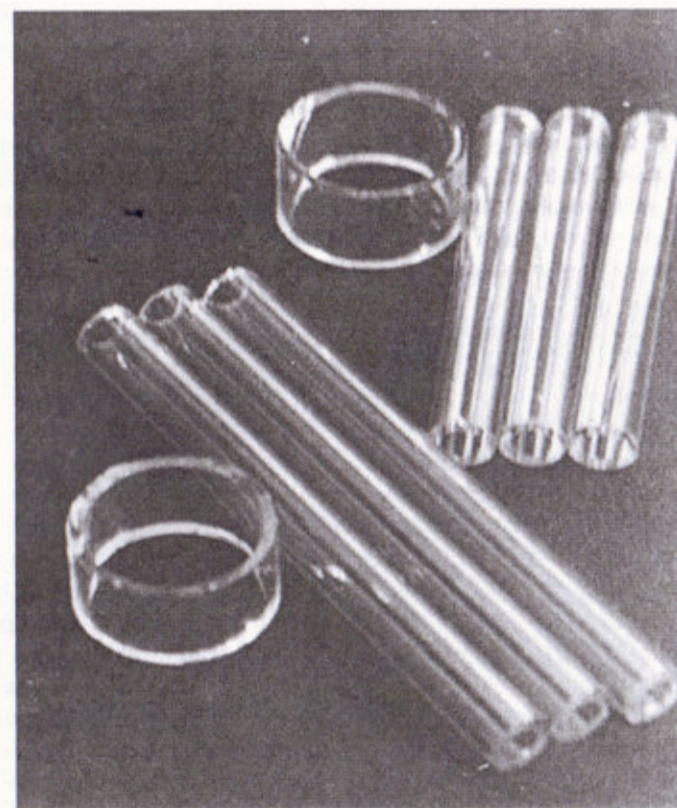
Образцы заготовок колец для плоской ножки ЭОС и штенгеля полученные на установках В2.М3.104.012 и В2.М3.104
